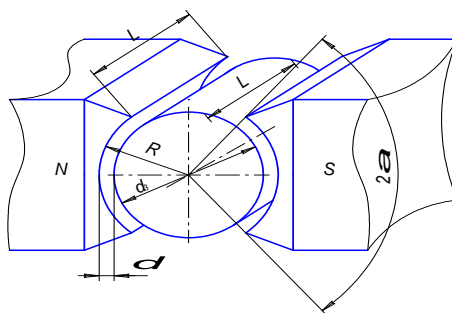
Форма рабочего зазора при MAO цилиндрических поверхностей
